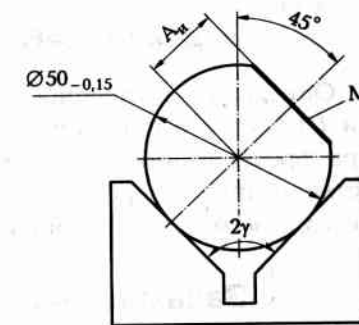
Схема установки заготовки на призму при фрезеровании плоскости
